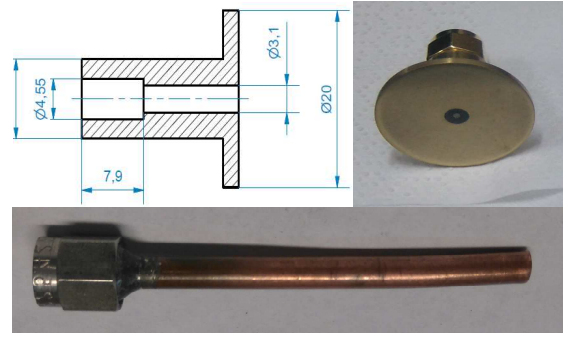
Izquierda arriba: Corte lateral y dimensiones del cabezal plano exterior (en mm). Derecha arriba: Ensamble del cabezal. Abajo: Cable semirrígido UT-141 utilizado.
